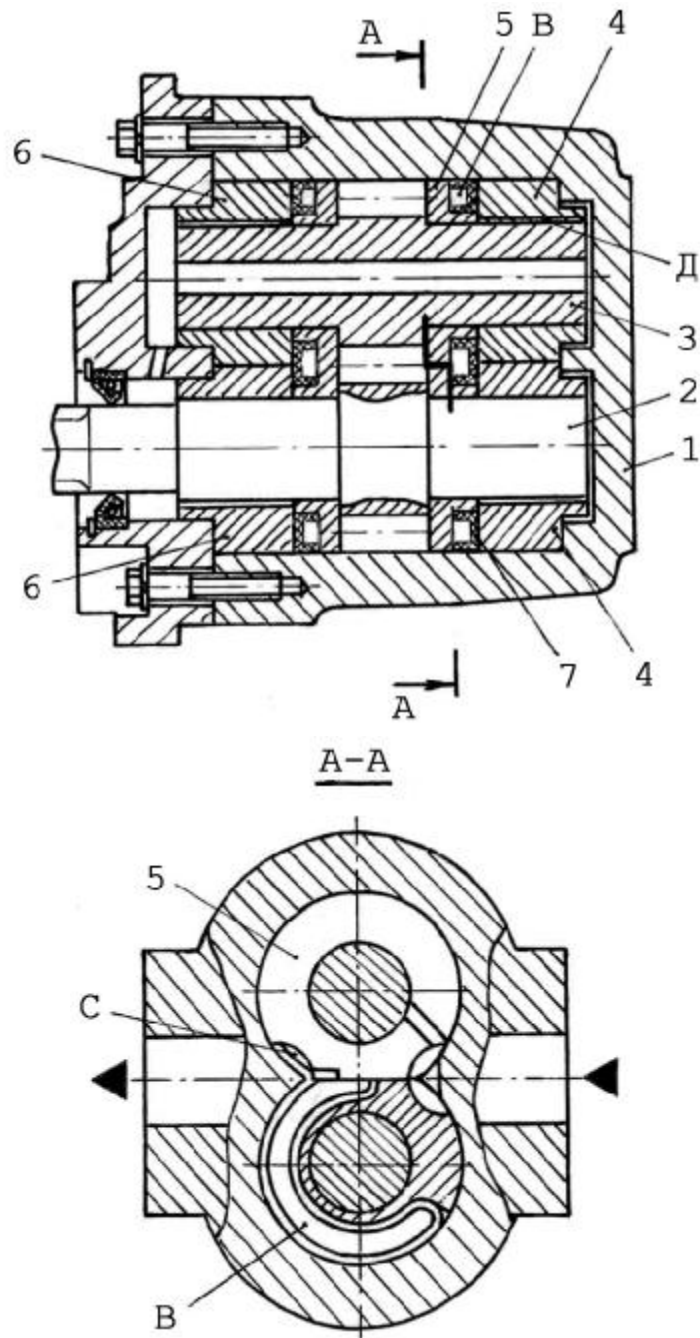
гидронасос НШ – 32У: 1 – корпус; 2 и 3 – ведущий и ведомый валы; 4 и 6 - втулки; 5 – поджимная пластина; 7 – манжета; В и С – полости давления; Д – канал.
